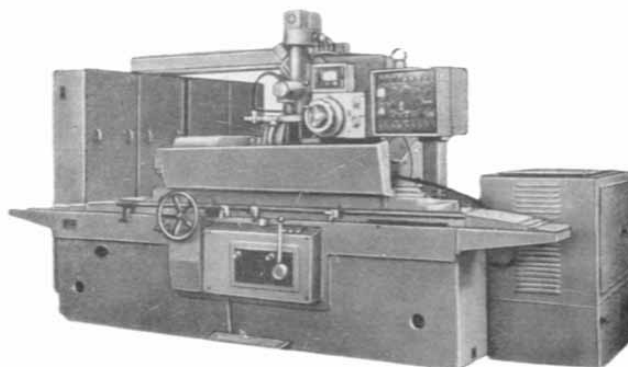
Станок круглошлифовальный с ЧПУ 3M151Ф2
